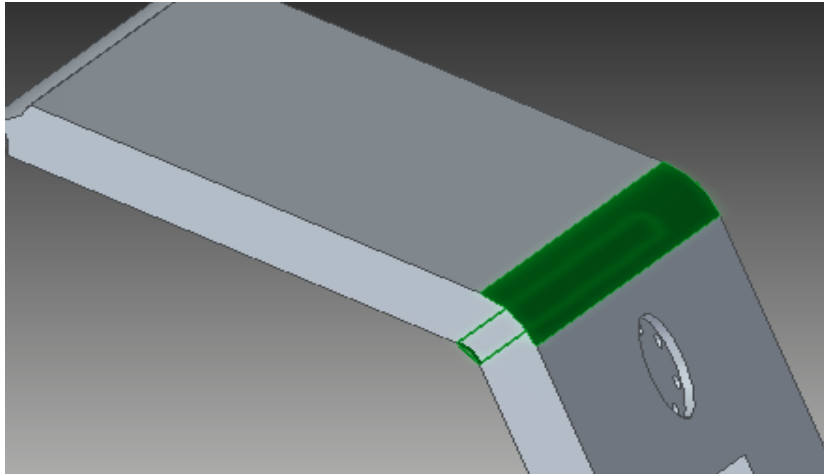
Fase di piegatura della lamiera durante la modellazione del telaio
